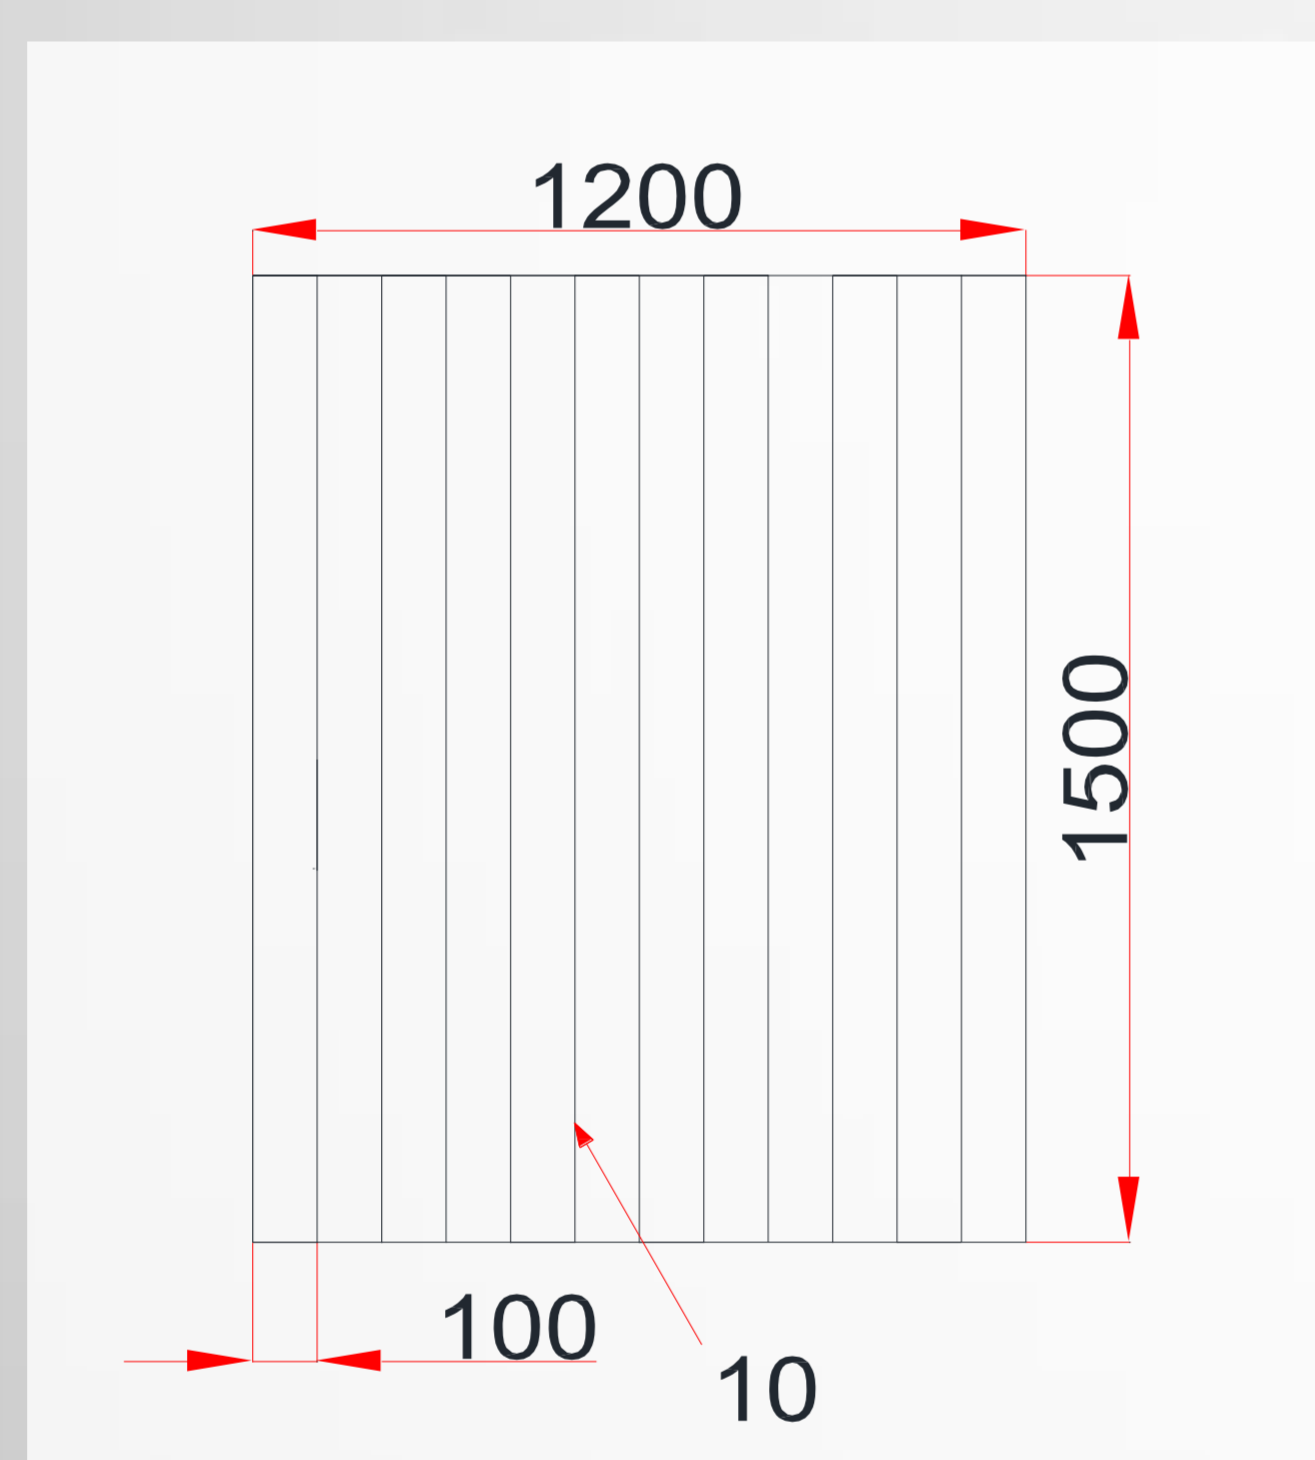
Esquema de la grilla diseñada. (Medidas en mm)
